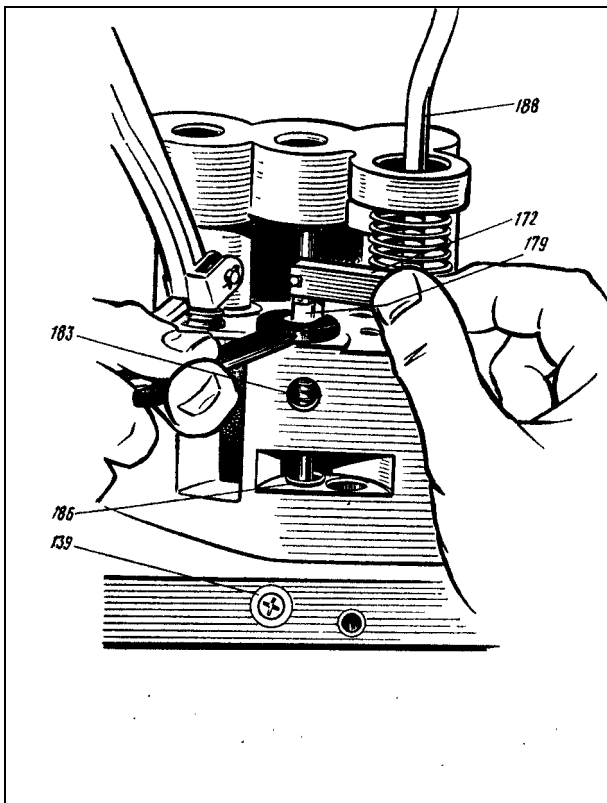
139—игла изодрома; 172—плавающий рычаг; 179 — наконечник штока принимающего поршня изодрома; 183— пружина изодрома; 186— принимающий поршень изодрома; 188—штанга задающего поршня изодрома
